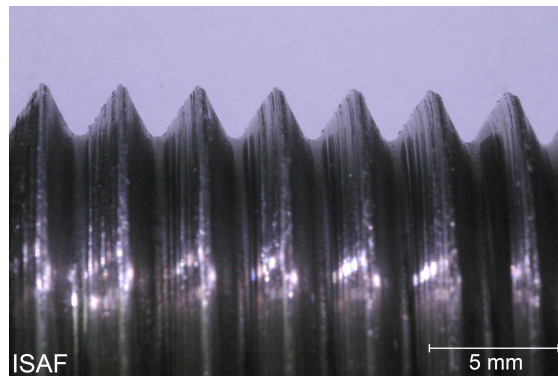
Gewindeprüfkörper axial belastet mit 100kN (Bolzen)
